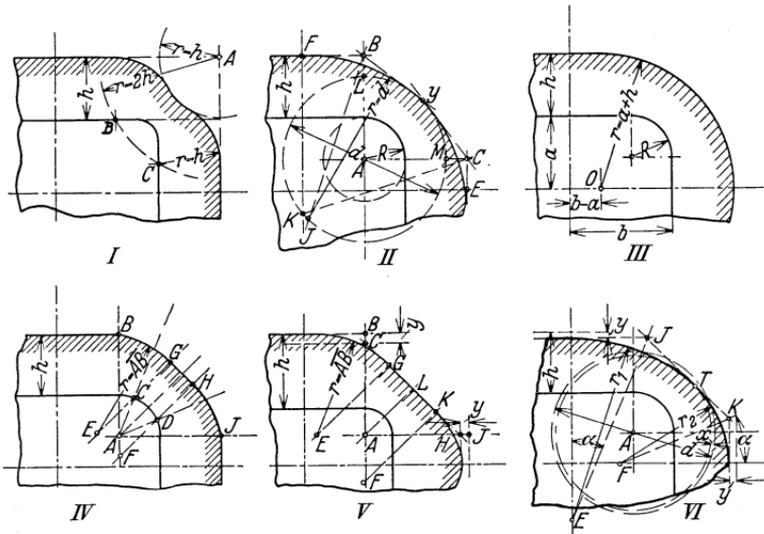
Zuschnittsformen rechteckiger Kappen.
